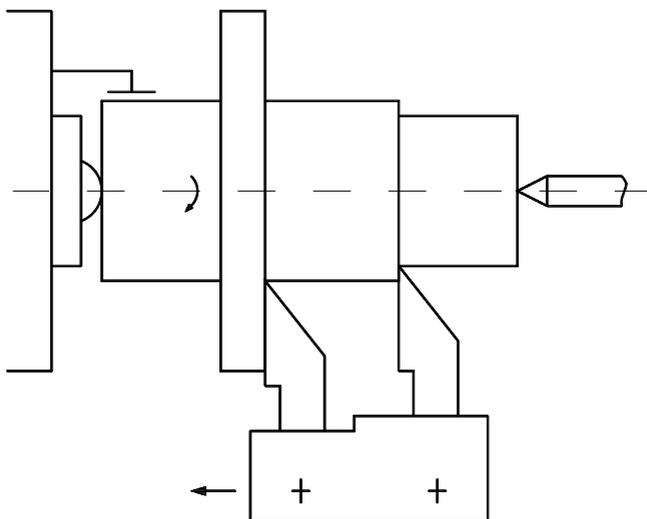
Пример обработки поверхностей ступенчатого вала за один переход
